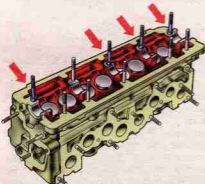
Установочные втулки корпусов подшипников распределительного вала
